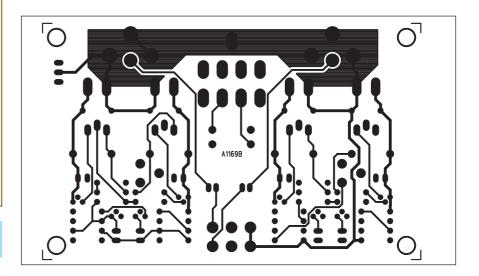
Obrazec desky spojů stereofonního zesilovače (strana BOTTOM)
